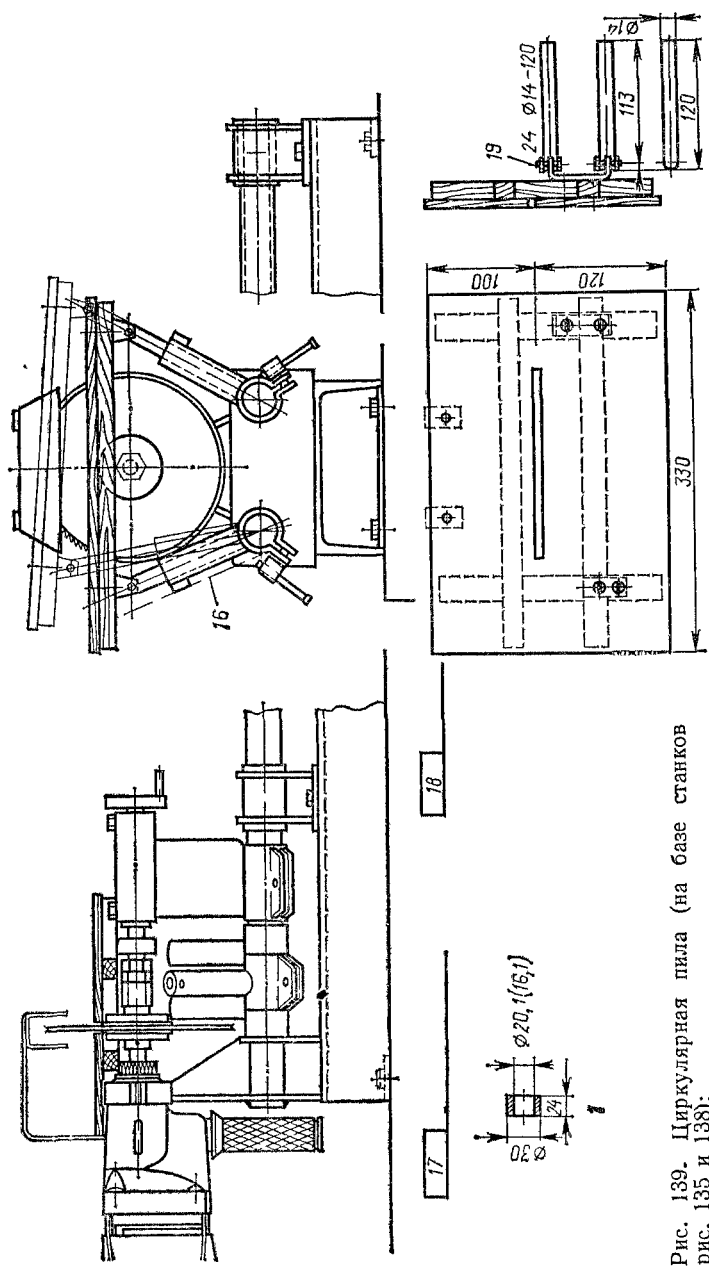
Циркулярная пила (на базе станков рис. 135 и 138):
